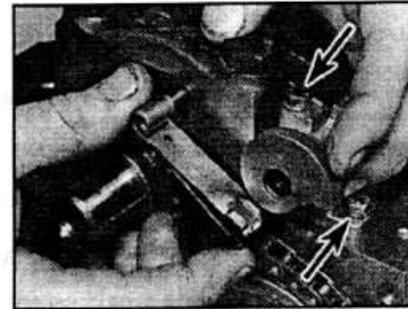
А.18. Поворот кулачка натяжителя и снятие рычага натяжителя цепи. Стрелками показаны болты крепления натяжителя цепи.
